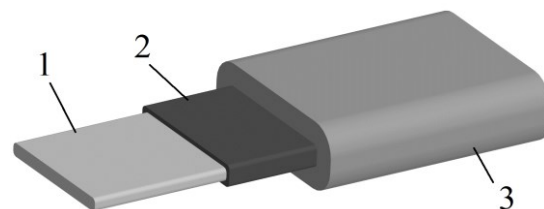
Образец без ферромагнитной ленты для сравнения (макет силового реактора)
